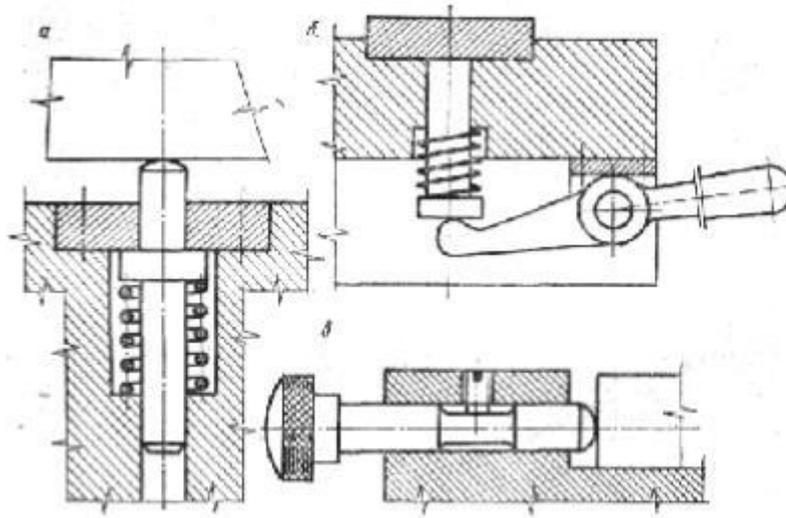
Выталкиватели ( а – пружинный; б – рычажный; в- кнопочный)
